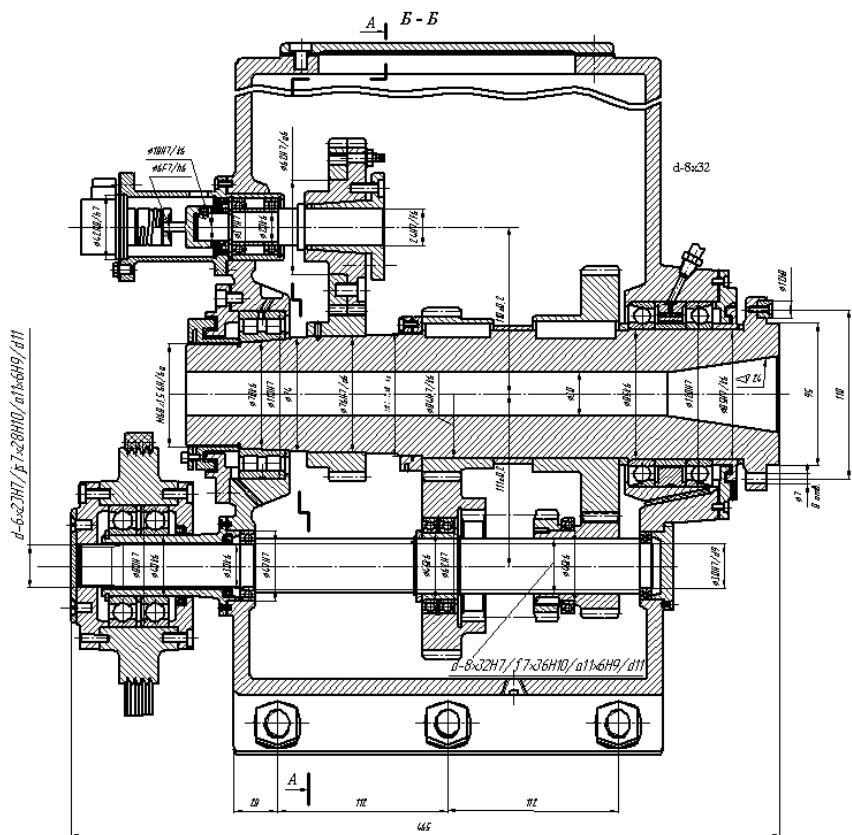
Шпиндельная бабка токарного станка с ЧПУ с наклонной станиной с двухступенчатой коробкой скоростей
